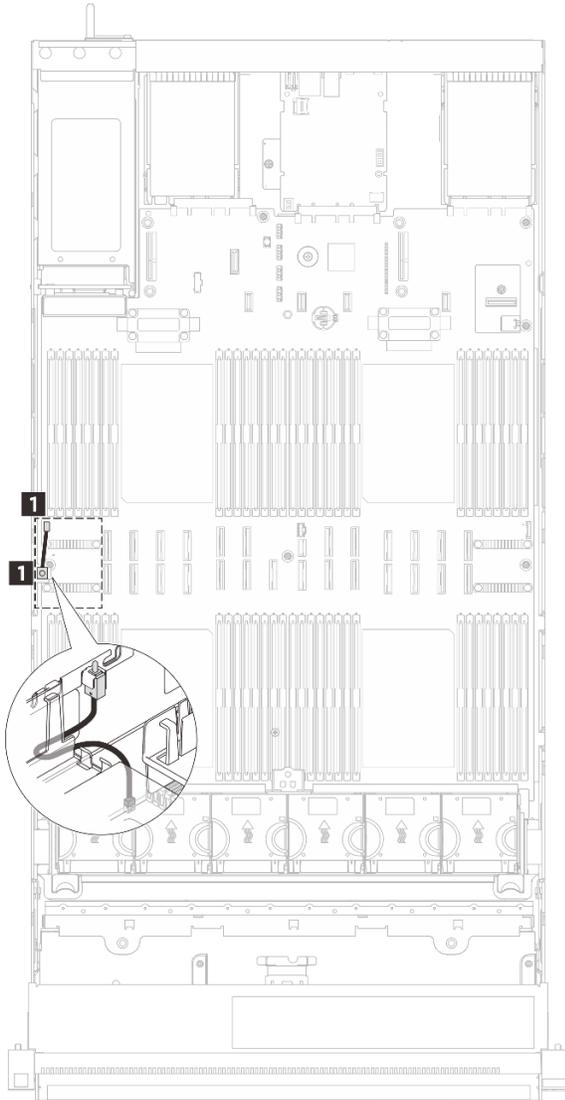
Kabelführung für den Schalter gegen unbefugten Zugriff
